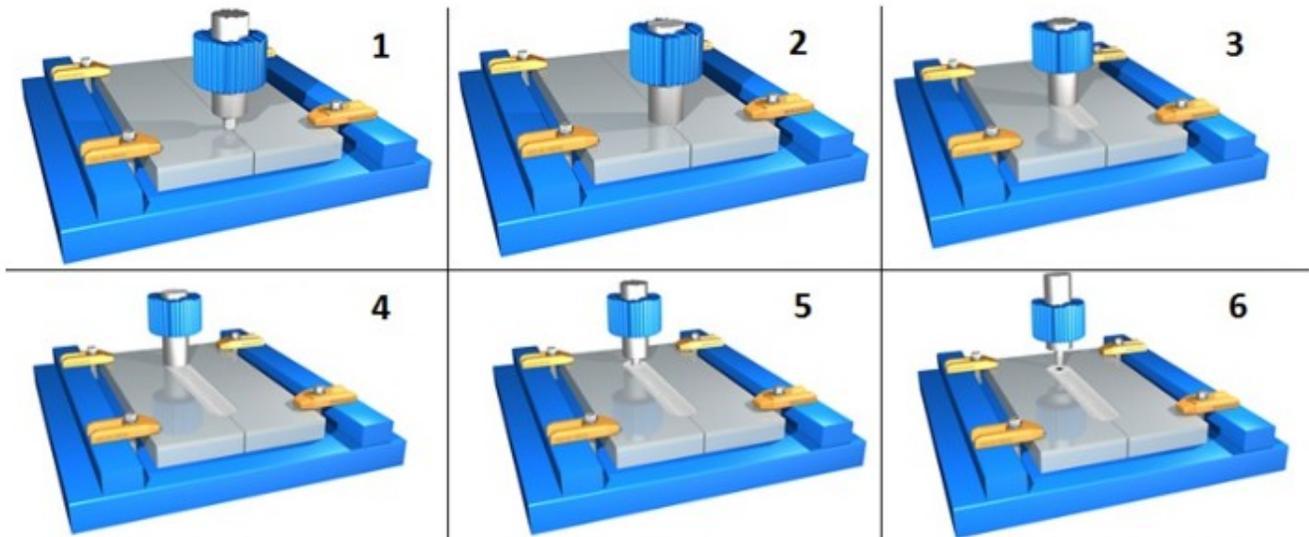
Soldadura por fricción - agitación.
